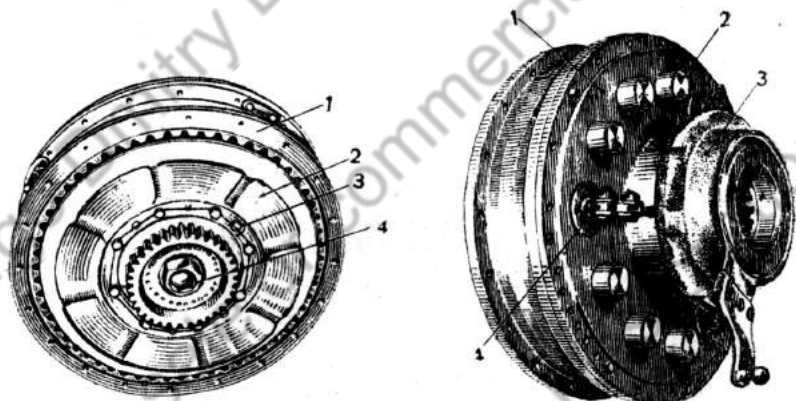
Главный фрикцион (общий вид со стороны коробки перемены передач): 1 — ведущий барабан; 2 — опорный диск; 3 — подвижная чашка выключенная; 4 — натяжной валик
